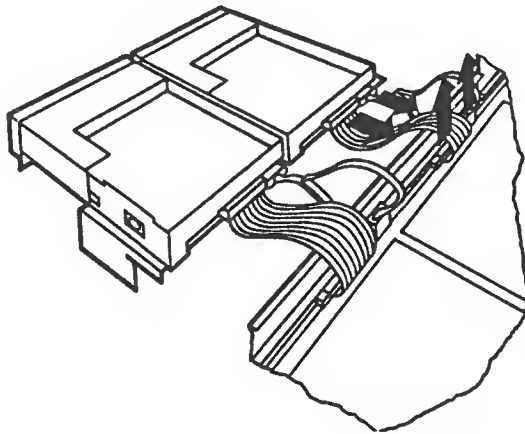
Kabel vom Diskettenlaufwerk entfernen
